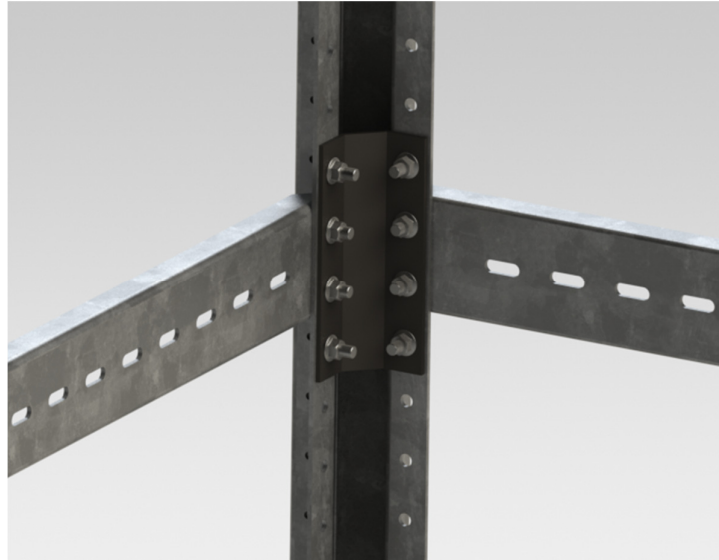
Utilização da peça de ligação exterior na zona de união com as travessas.
